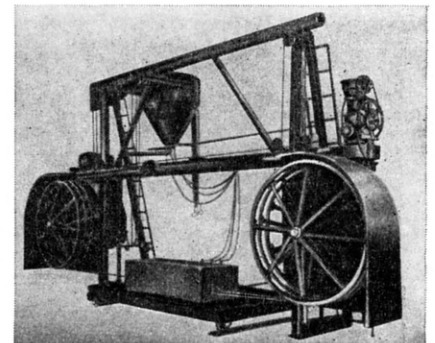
Канатная пила для выпиливания блоков камня в карьере: 1 — приводная станция; 2 — неразвивающийся канат; 3 — натяжное приспособление; 4 — пильные стойки.
